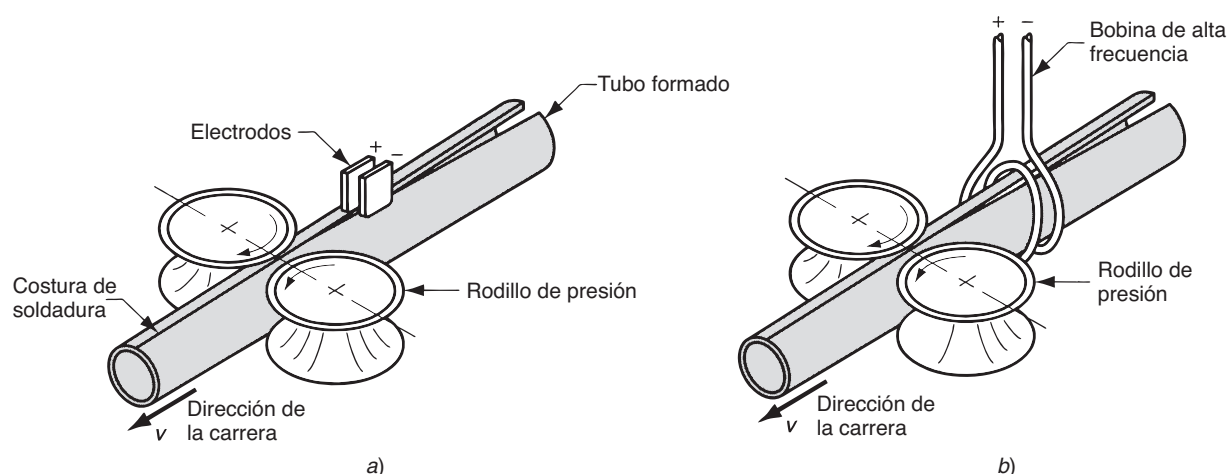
Soldadura de tubos con costura, mediante a) soldadura por resistencia de alta frecuencia y b) soldadura por inducción de alta frecuencia.
